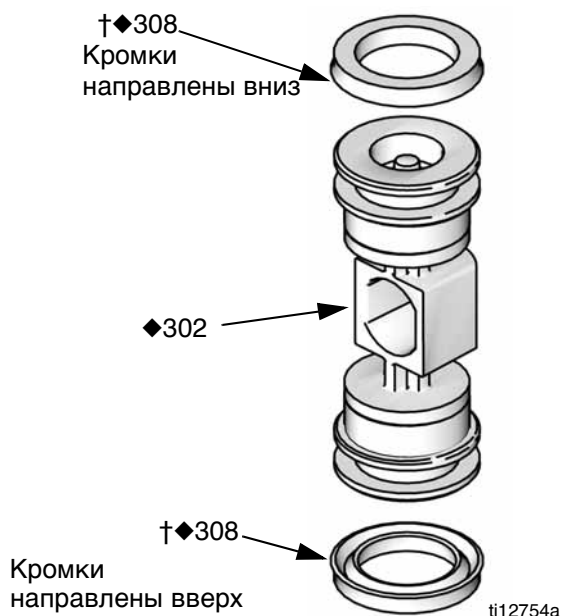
Установка П-образных уплотнительных колец воздушного клапана
